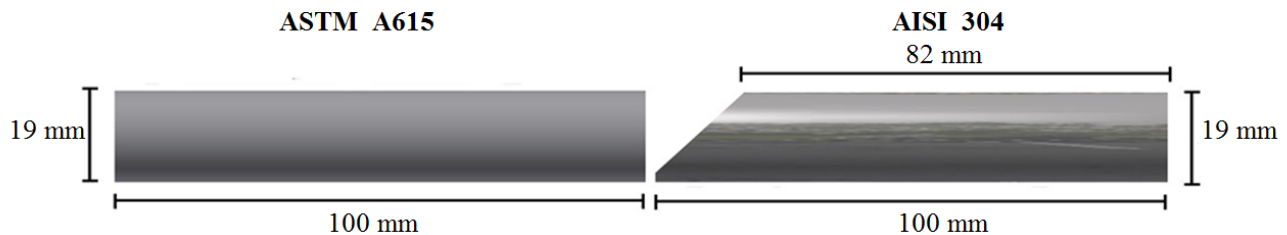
Diagrama esquemático do bisel simples das juntas soldadas de metais diferentes. A barra da esquerda consiste de aço carbono ASTM A615 e a barra da direita é de aço inoxidável AISI 304.
